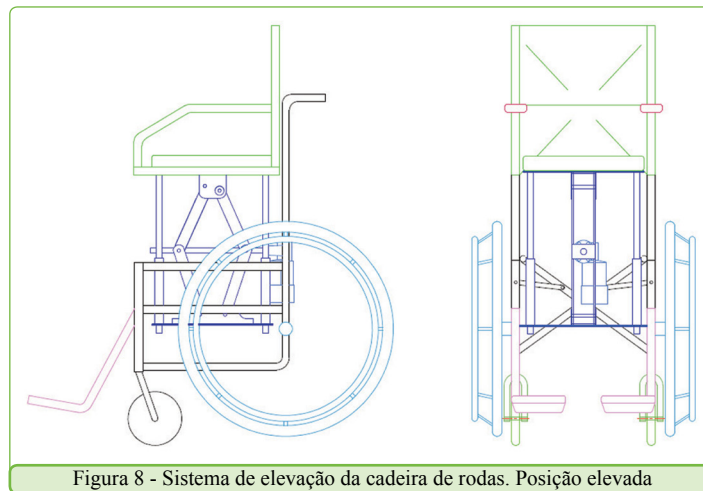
Sistema de elevação da cadeira de rodas. Posição elevada
